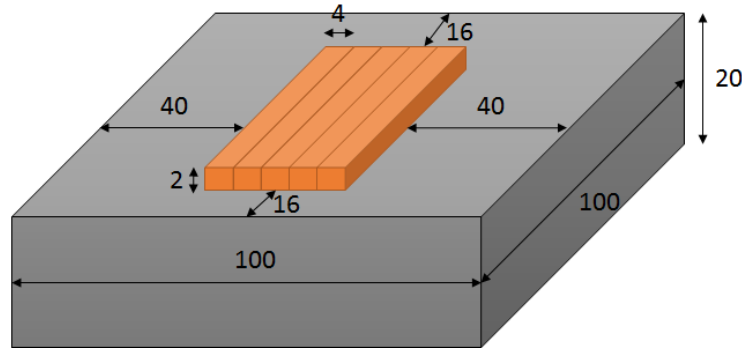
Géométrie du cas test de soudage multipasse.
